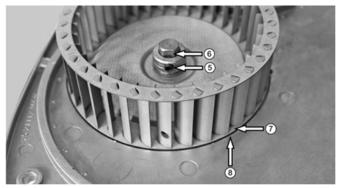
Axiale Positionierung des Gebläserades Legende zu Abb. 28:
